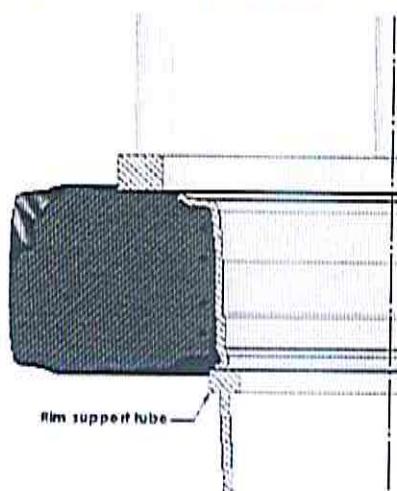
Схема расположения колеса при выпрессовке диска
